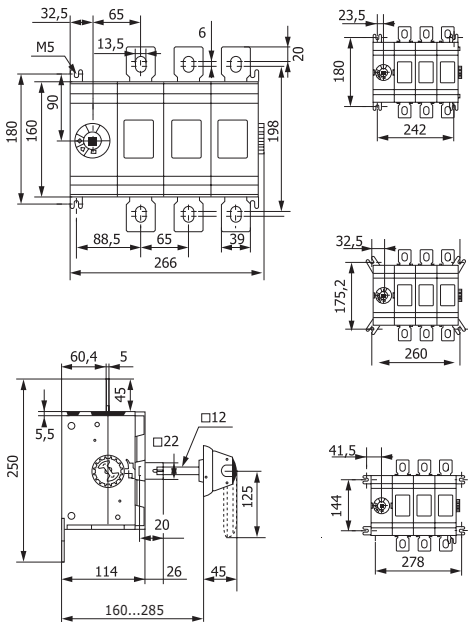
Габаритные и установочные размеры рубильников 630-800 А 3Р
